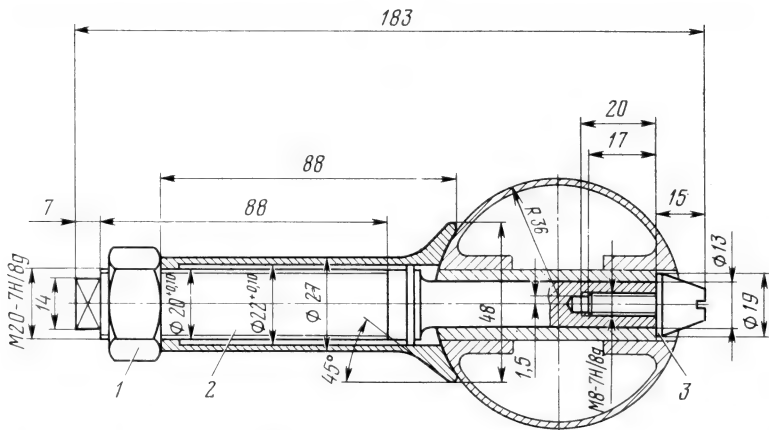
Приспособление для выпрессовки поршневого пальца:
